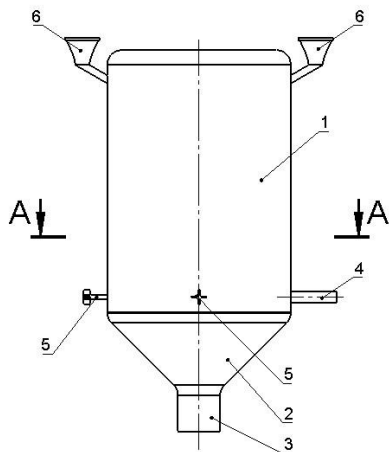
Конструкция пневмосмесителя (вид спереди):
